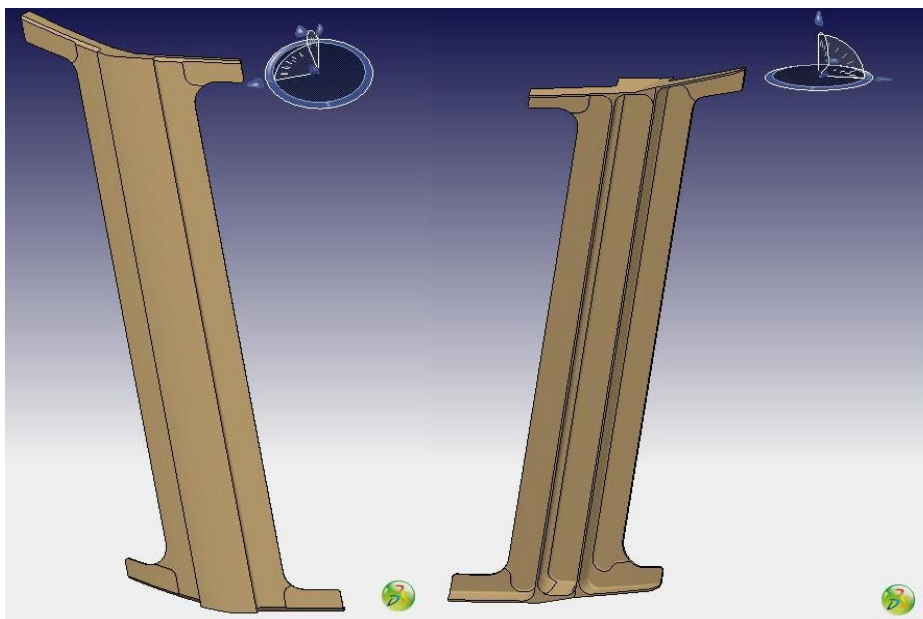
Proposta de alteração da viga lateral da estrutura.
